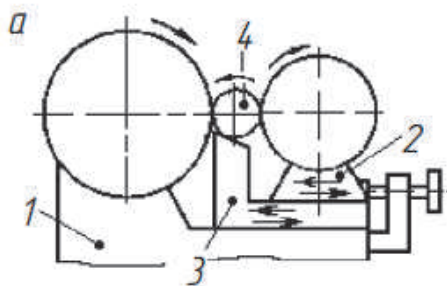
Схема установки центра заготовки под линией центров шлифовального и ведущего кругов [1]
